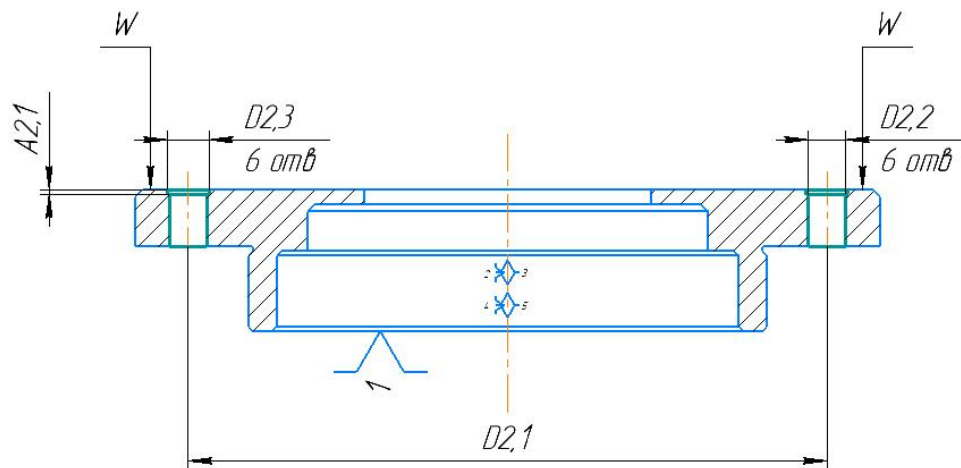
,1 - Принципиальная схема зажима заготовки в приспособлении с указанием мест приложения силы зажима.
